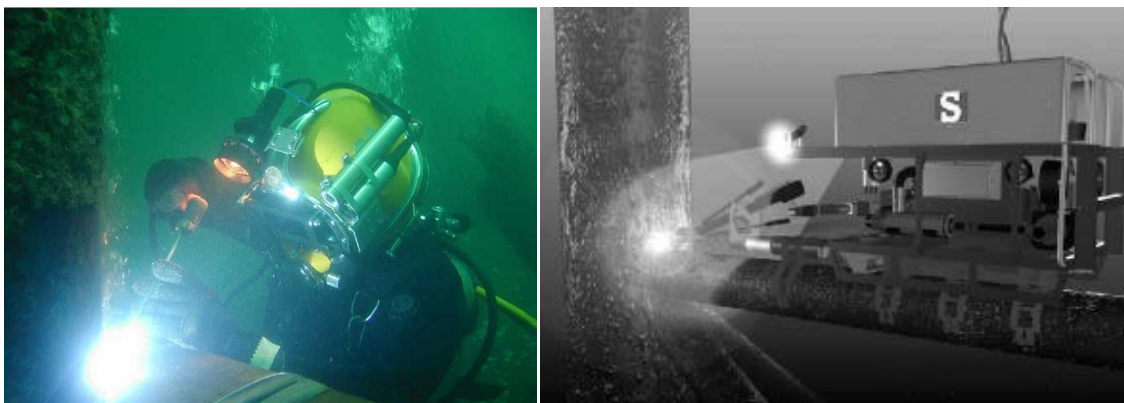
(A) Soldagem subaquática com eletrodo revestido; (B) ROV com equipamento de solda por FHPP acoplado a estrutura de uma plataforma (MEYER 2001).
